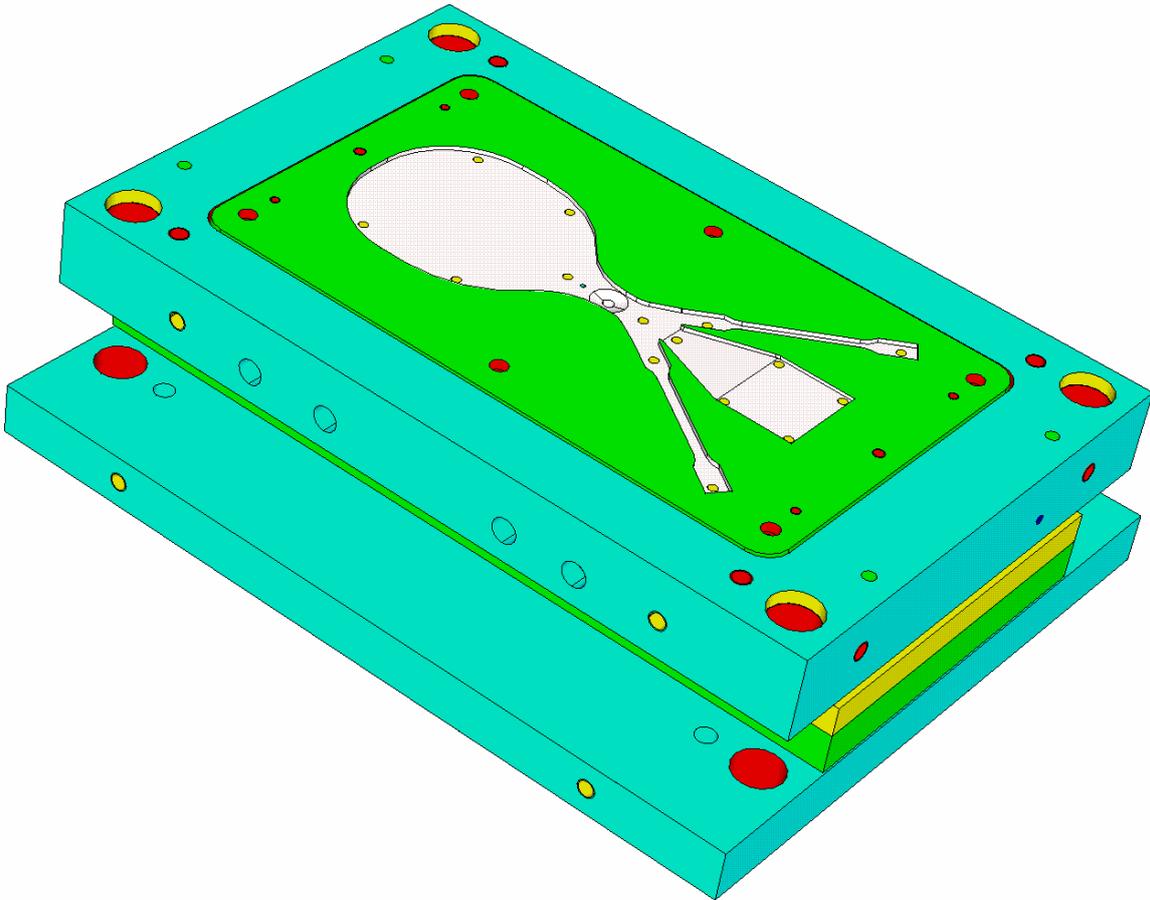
CAD-Bild der Multiprobekörperwerkzeugkavität
